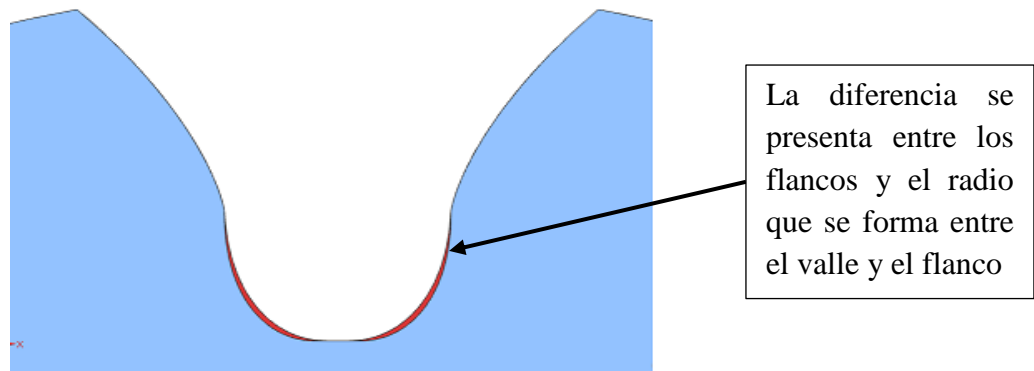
Superposición de los engranajes generados a partir del acelerador de diseño
